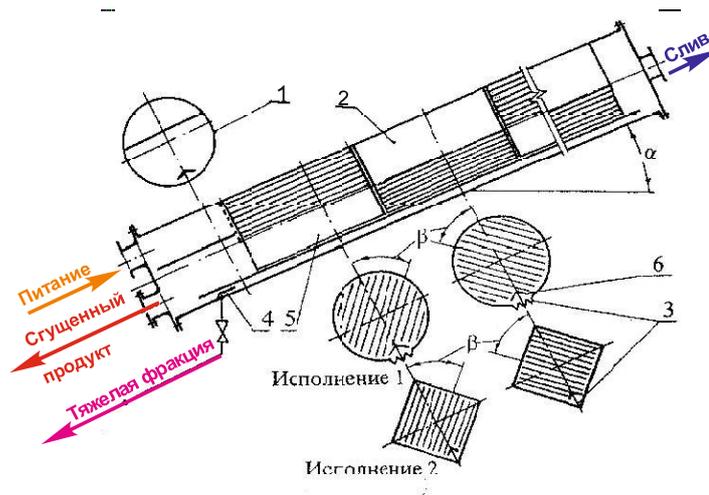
Компоновочный вариант конструкции тонкослойного аппарата: 1 – оболочка; 2 – тонкослойные секции; 3 – продольные (гофрированные) каналы; 4 – отсекающий карман; 5 – пластины; 6 – экран / Fig. 2. Layout version of the thin-layer device design: 1 – shell; 2 – thin-layer sections; 3 – longitudinal (corrugated) channels; 4 – cutting pocket; 5 – plates; 6 – screen
